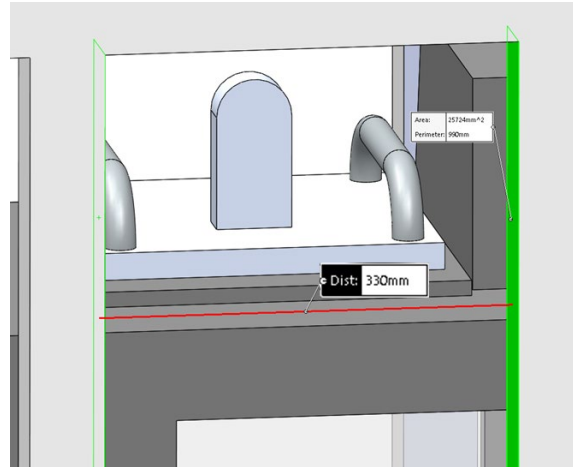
Espaçamento entre os pilares da estrutura de apoio da balança.
